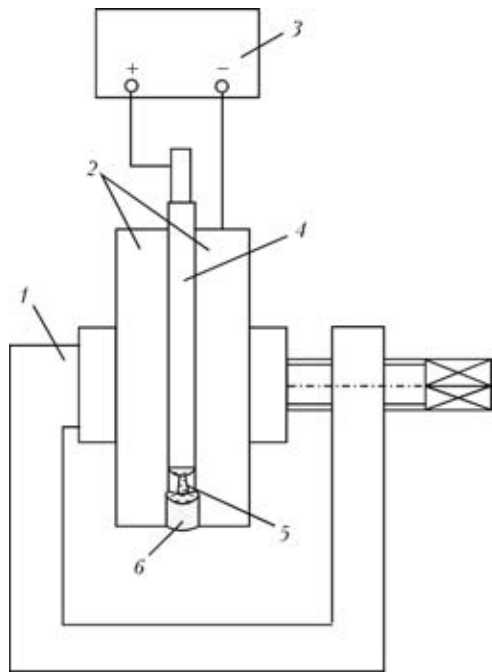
Схема сварки стыка пластин с зазором 1,5 мм: 1 — трубина; 2 — свариваемые части; 3 — источник тока; 4 — пластинчатый электрод; 5 — электрическая дуга; 6 — сварной шов
